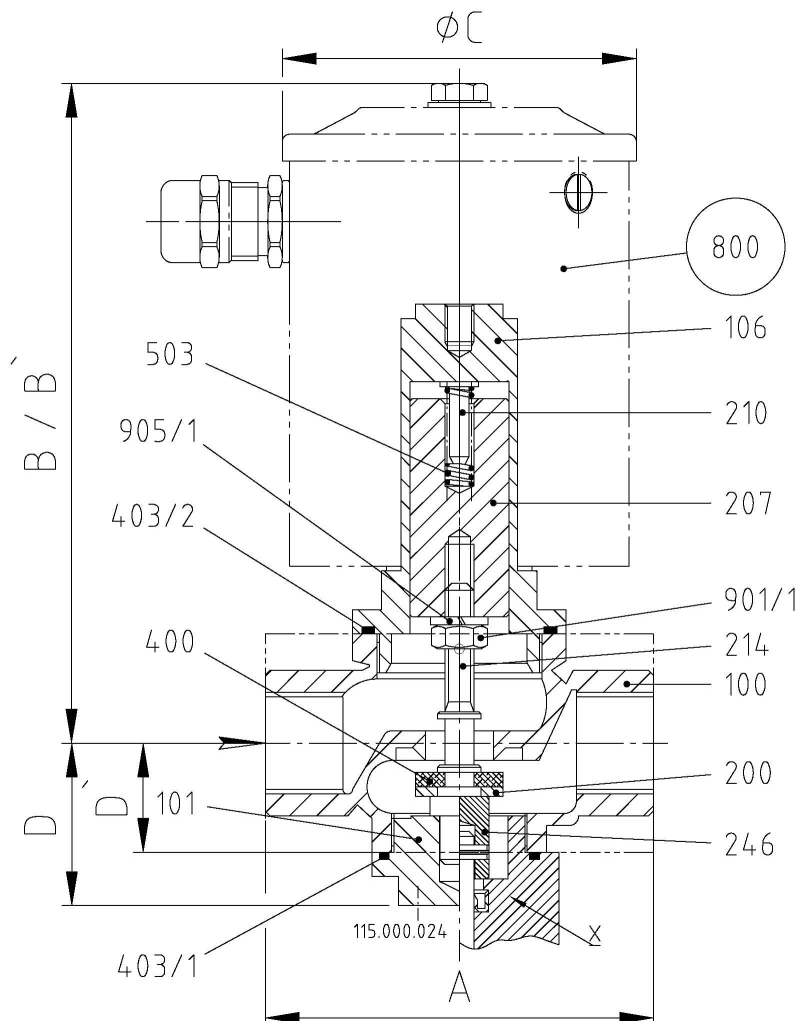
Gewindeausführung: 6- EVO 3/5R
